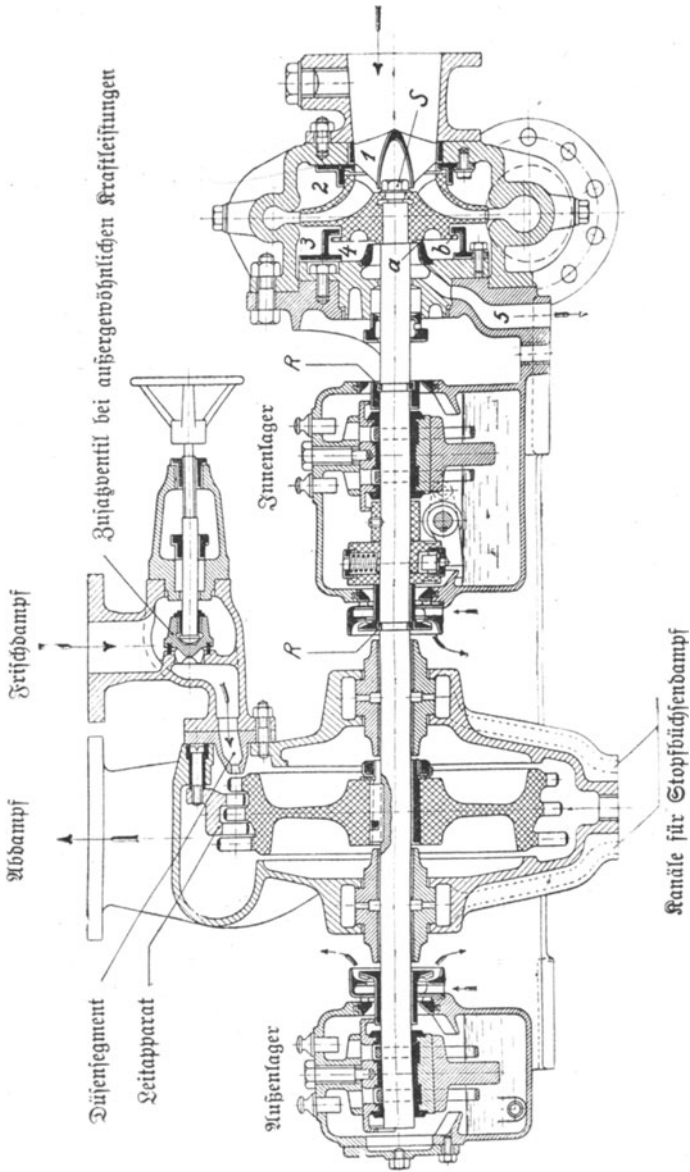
Längsschnitt durch die Turbopfelepumpe.
